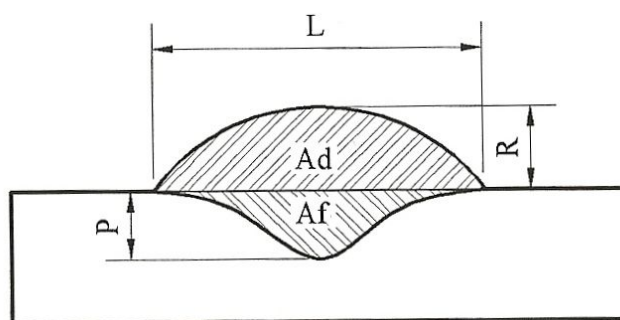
Representação esquemática das dimensões geométricas das seções transversais dos cordões/revestimentos soldados.⁽⁴⁾
